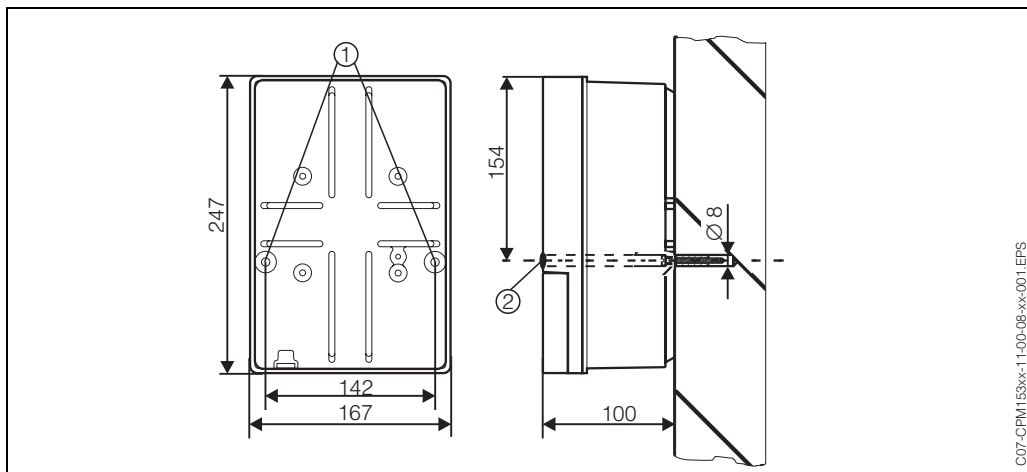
Dimensions pour montage mural : vis de fixation : \varnothing 6 mm, cheville : \varnothing 8 mm
